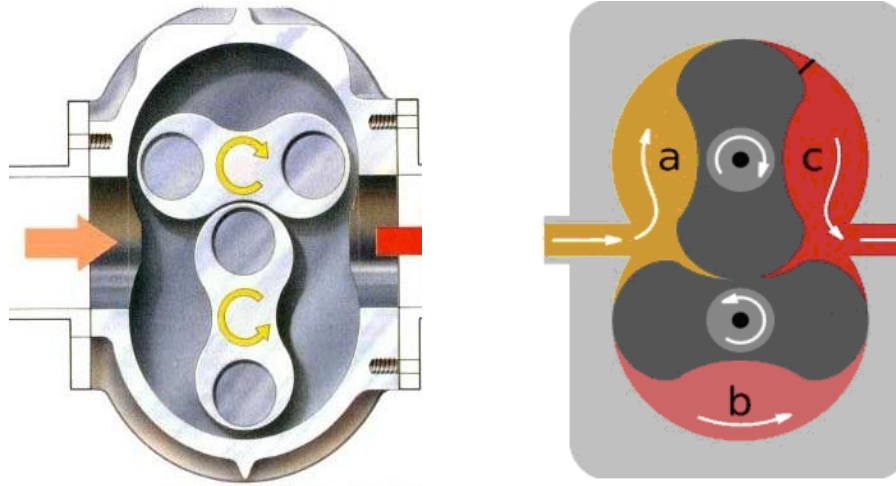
Поперечный разрез роторного компрессора и схема продвижения воздуха в его каналах
